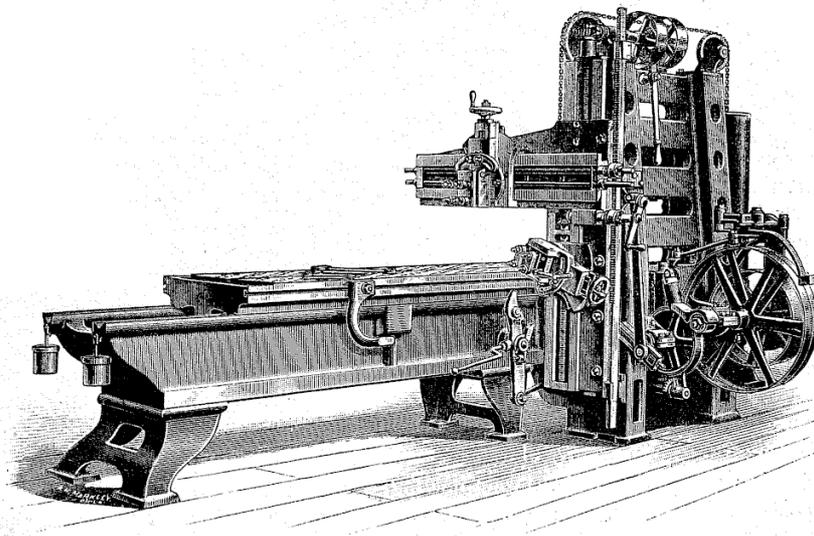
Raboteuse latérale Detrick Harvey (Voir G. Richard, *Traité des machines-outils*, vol. I, p. 293).
